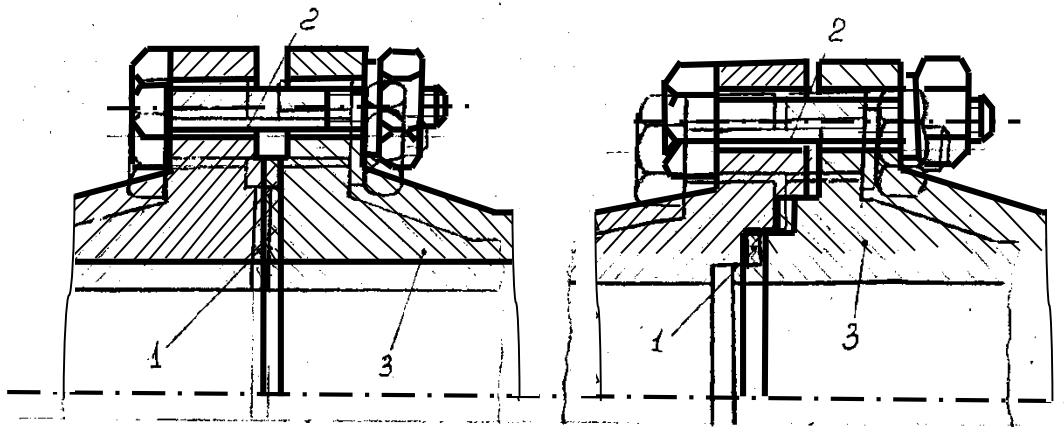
Фланцевые соединения с плоскими прокладками: 1 – прокладка, 2 – болтовое соединение, 3 – фланец трубопровода
